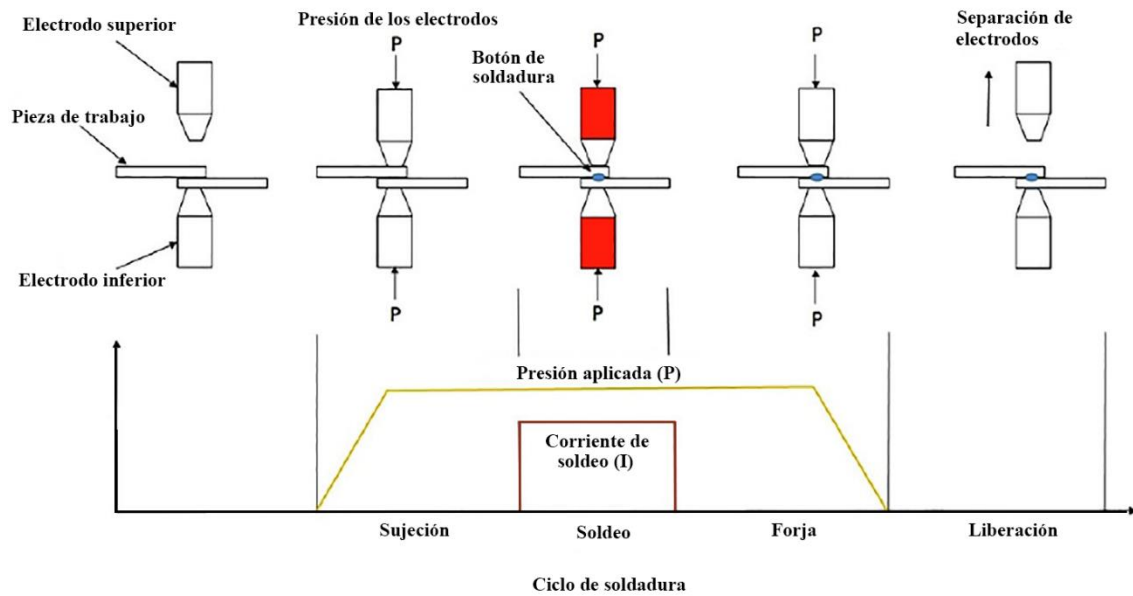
Etapas del ciclo térmico de la soldadura RSW [15].
